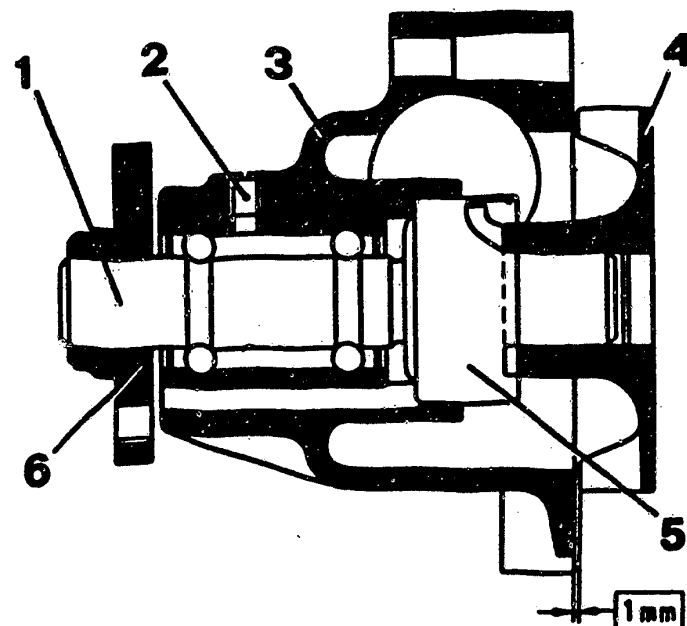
Schnitt durch die Wasserpumpe des Benzinmotors: 1 Pumpenwelle – 2 Lager-Befestigungsschraube – 3 Pumpengehäuse – 4 Schaufelrad – 5 Pumpenpackung – 6 Nabe.
